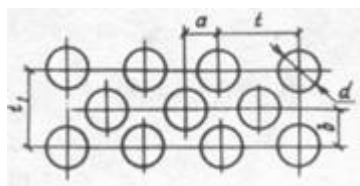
Схема шахматного расположения отверстий в барабане
